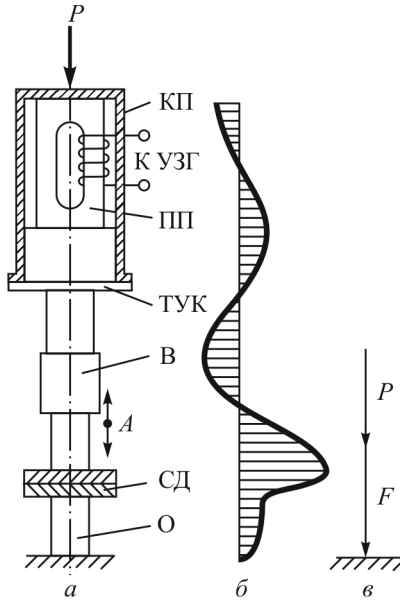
Ультразвуковая сварка с нормальным вводом колебаний: *а* – схема сварочного узла (КП – корпус преобразователя; ПП – пакет преобразователя с обмоткой; ТУК – трансформатор упругих колебаний; В – волновод; СД – свариваемые детали; О – опора;  $A$  – амплитуда смещения волновода); *б* – эпюра амплитуды смещения колебательной системы; *в* – расположение вектора статического давления  $P$  и динамического усилия  $F$
